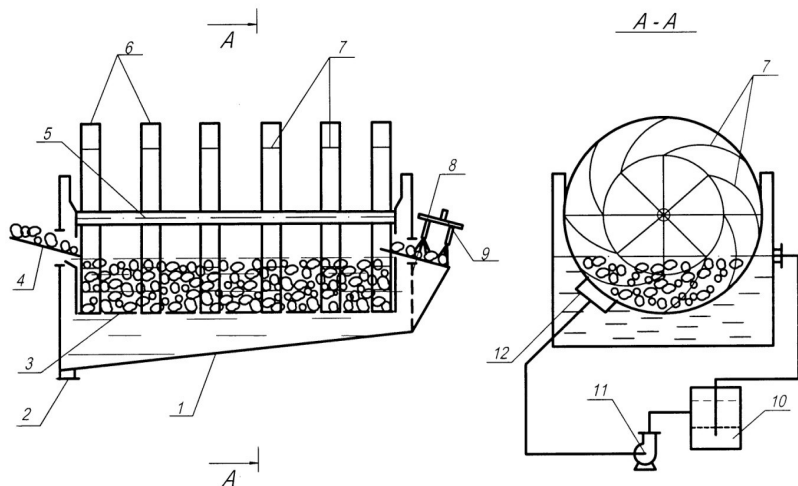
Схема барабанно–лопатевої мийки: 1–камера; 2– патрубок для видалення осілого бруду; 3 – мийна перфорована ванна; 4– ділянка завантаження; 5 – вал; 6 – циліндричні неширокі барабани; 7 – пластини; 8 – ділянка вивантаження; 9 – пристрій для ополіскування; 10 – ємність для фільтрування мийної води; 11 – насос; 12 – пристрій для подачі циркулюючої води
